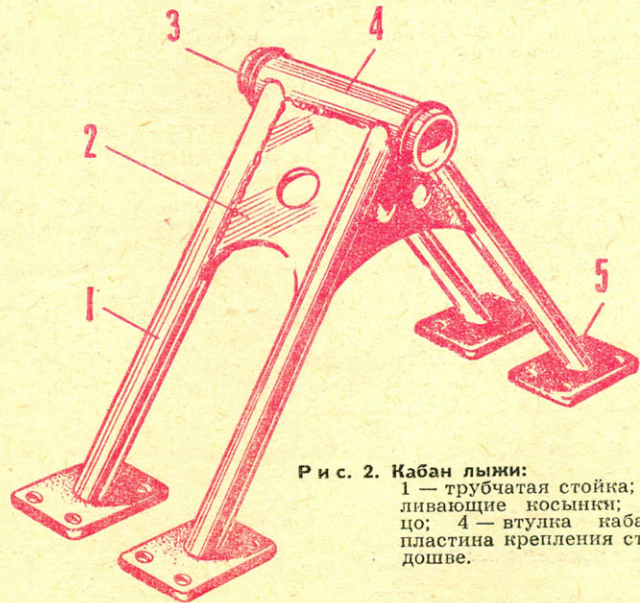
Кабан лыжи: 1 — трубчатая стойка; 2 — усиливающие косынки; 3 — кольцо; 4 — втулка кабана; 5 — пластина крепления стоек к подошве.
